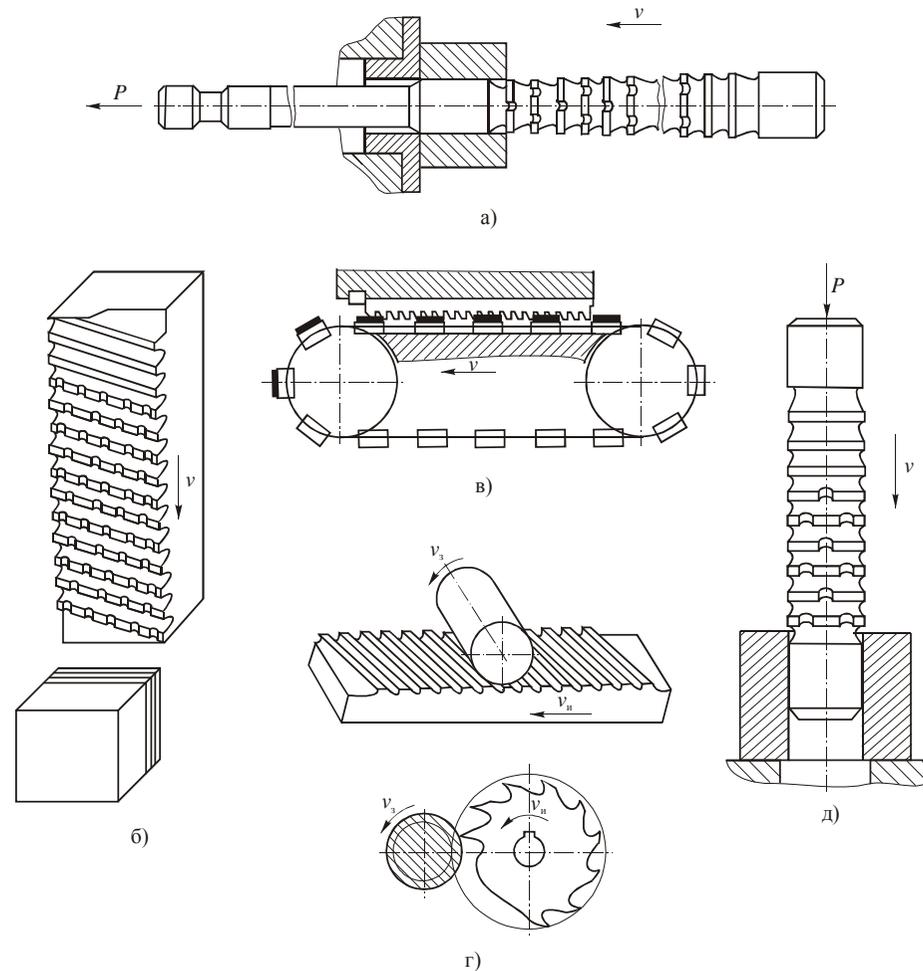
Схемы протягивания: *а* – отверстий; *б* – плоскостей; *в* – непрерывное протягивание наружной поверхности; *г* – обработка цилиндрической поверхности плоской и круглой протяжками; *д* – обработка отверстия прошивкой
